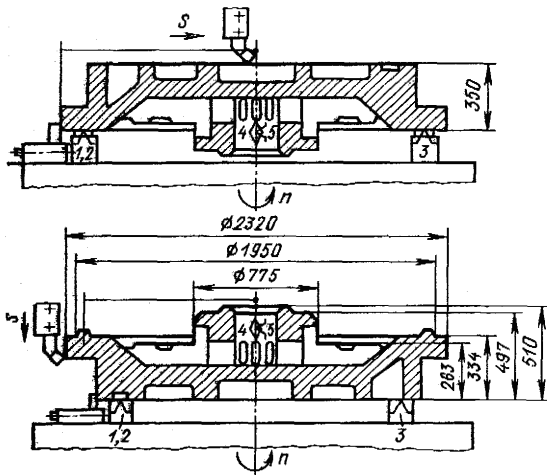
Обробка основи і кругових напрямних заготовки станини точінням на токарно-карусельному верстаті
